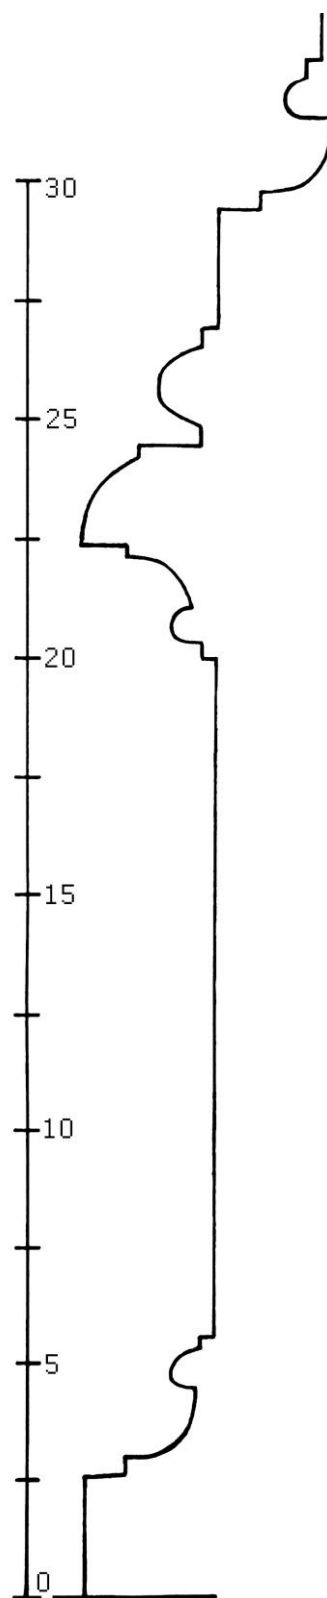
Profilace nohou pilastrů vysokých skříň.
